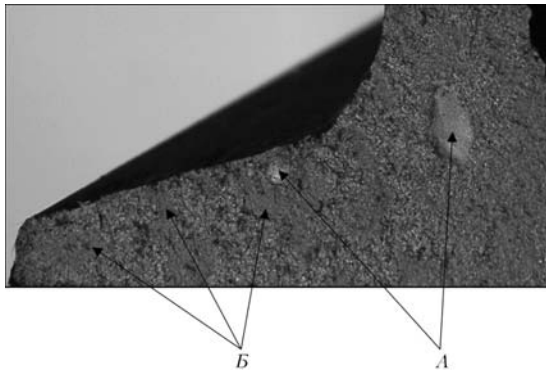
Фрагмент излома сварного соединения рельсов из стали Э76Ф: А — оксидные пленки; Б — МП
